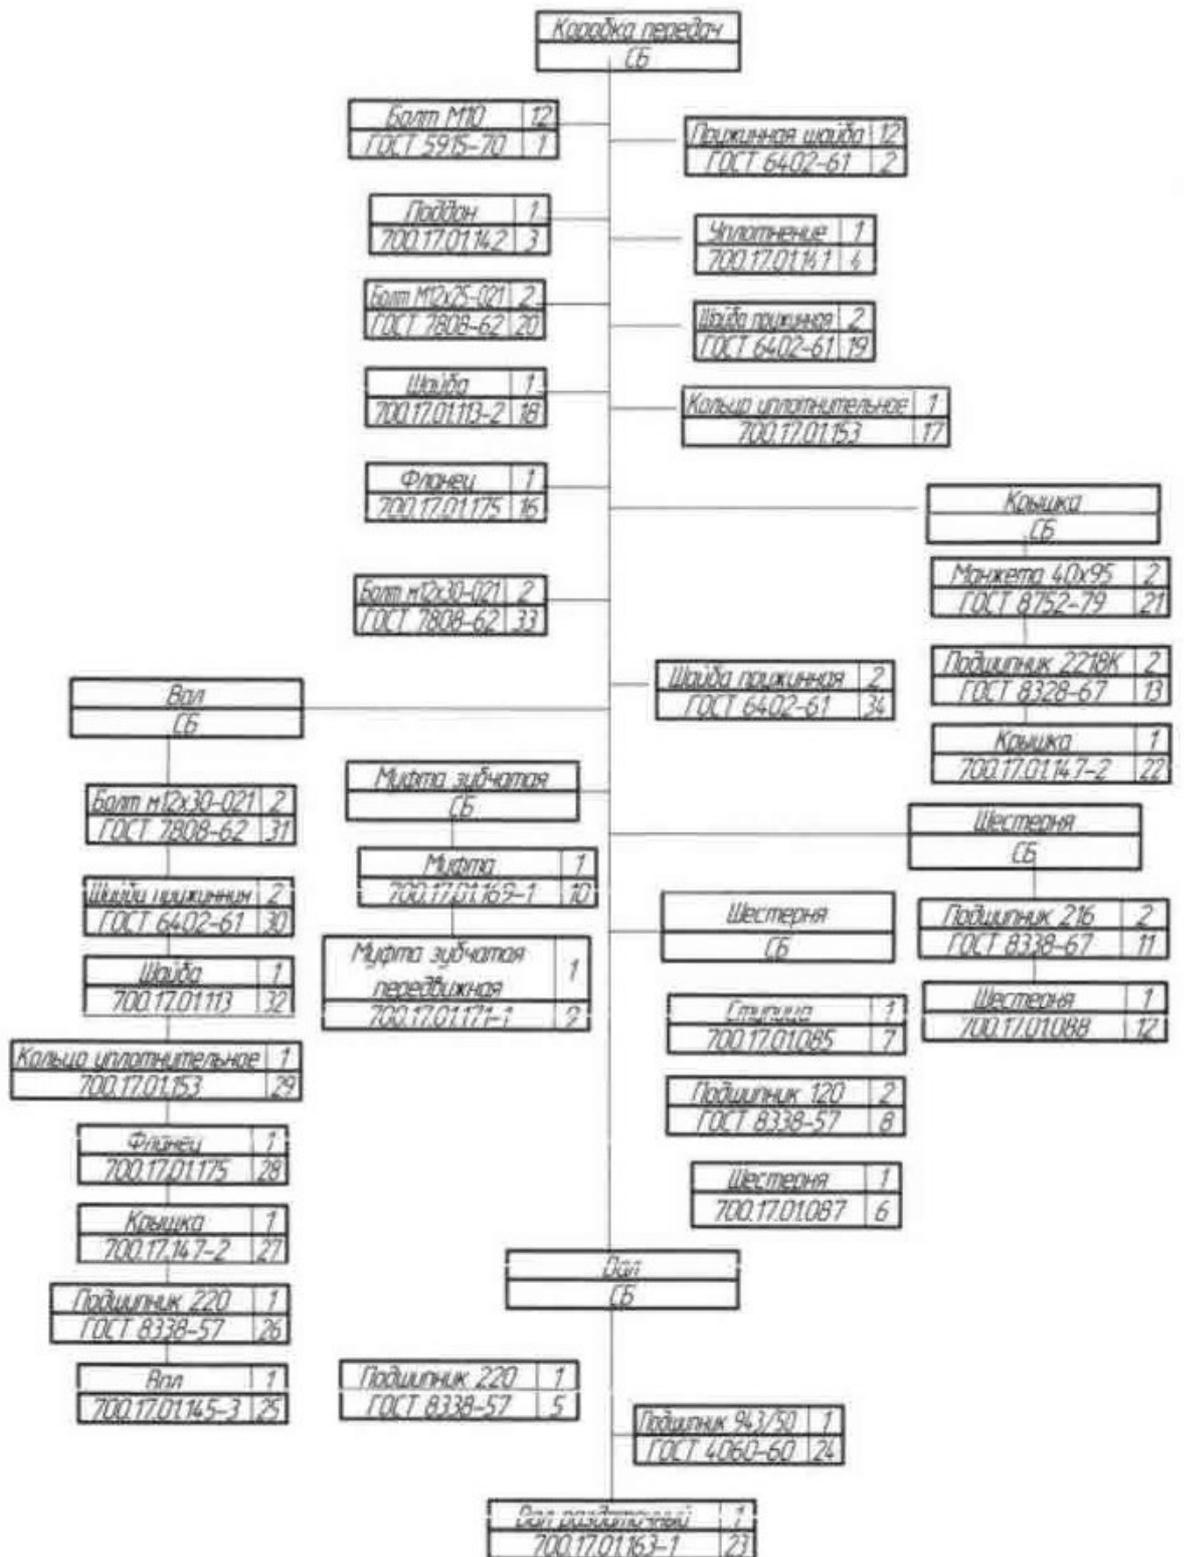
Структурная схема разборки коробки передач трактора К-
